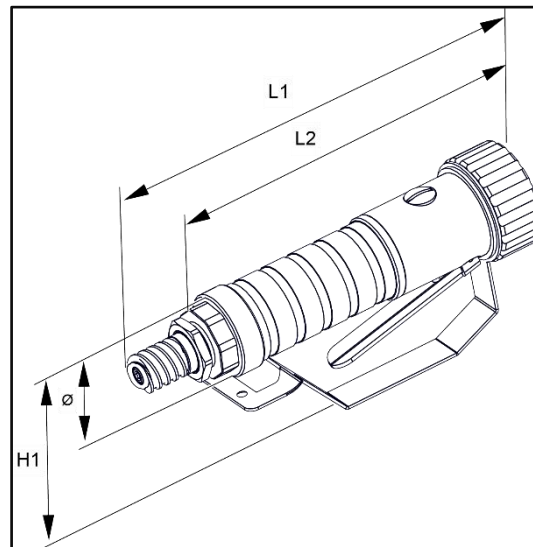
Gemonteerde Hand-Skinner HSK8-P3
